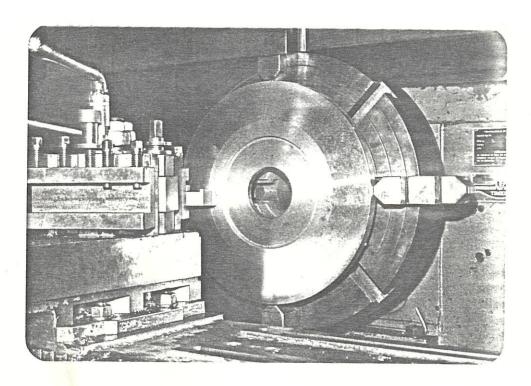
TORNEADO DEL DISCO DE LA TURBINA
